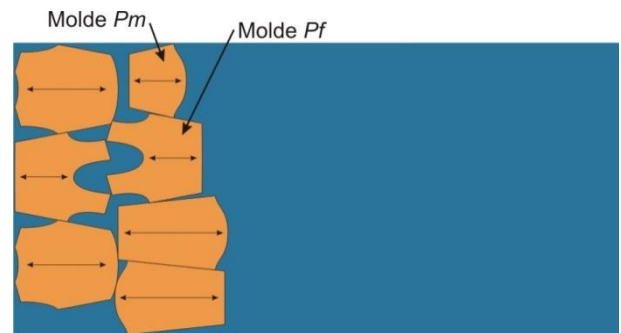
Inserção do molde que atinge a parte superior do tecido.
